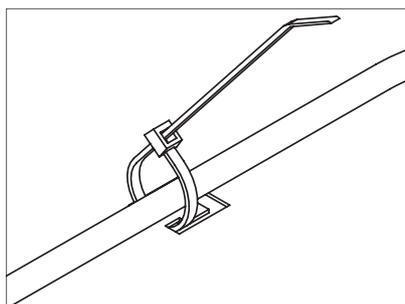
Fissare i cavi con una fascetta per cavi come scarico della trazione
